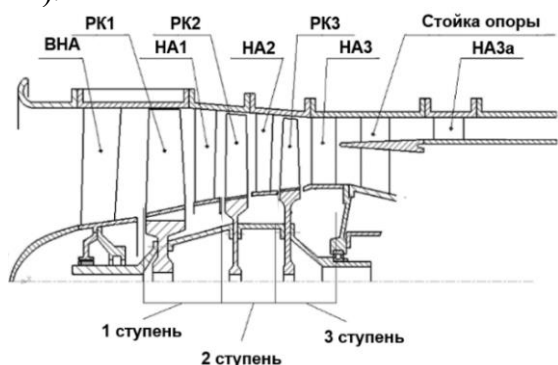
Схема компрессора низкого давления турбореактивного двухконтурного двигателя (базовый МОК)
